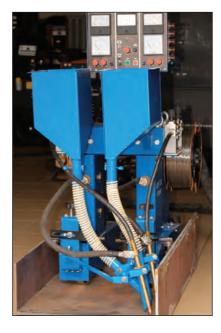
Вариант исполнения автомата для сварки под флюсом
